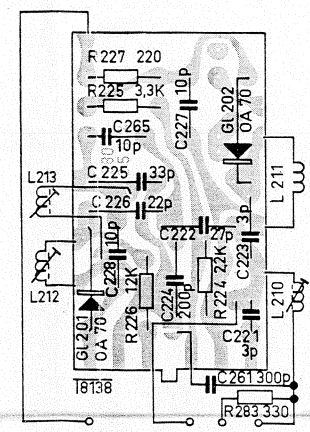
3. ZF-Leiterplatte mit Bestückung.
